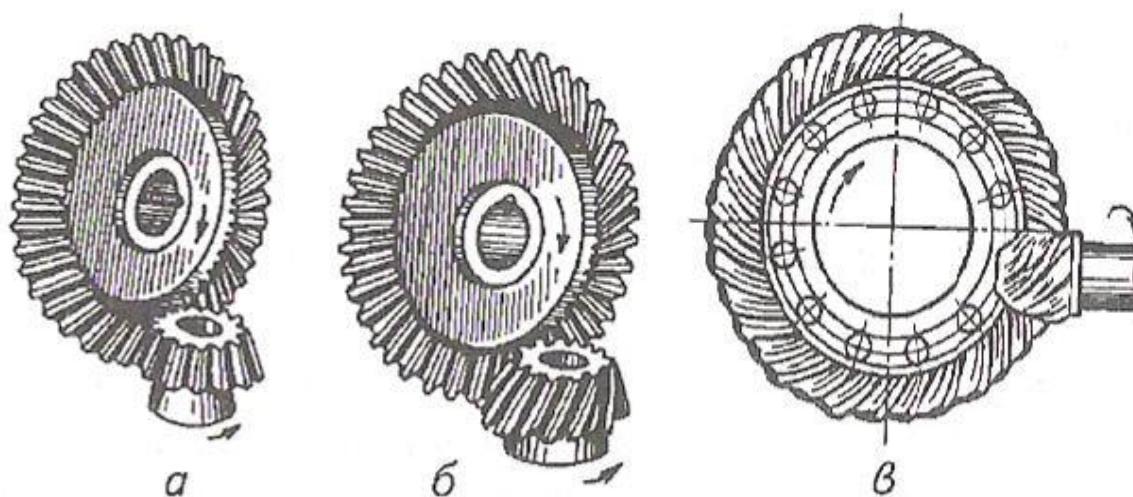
Типы главных передач тракторов и автомобилей:
